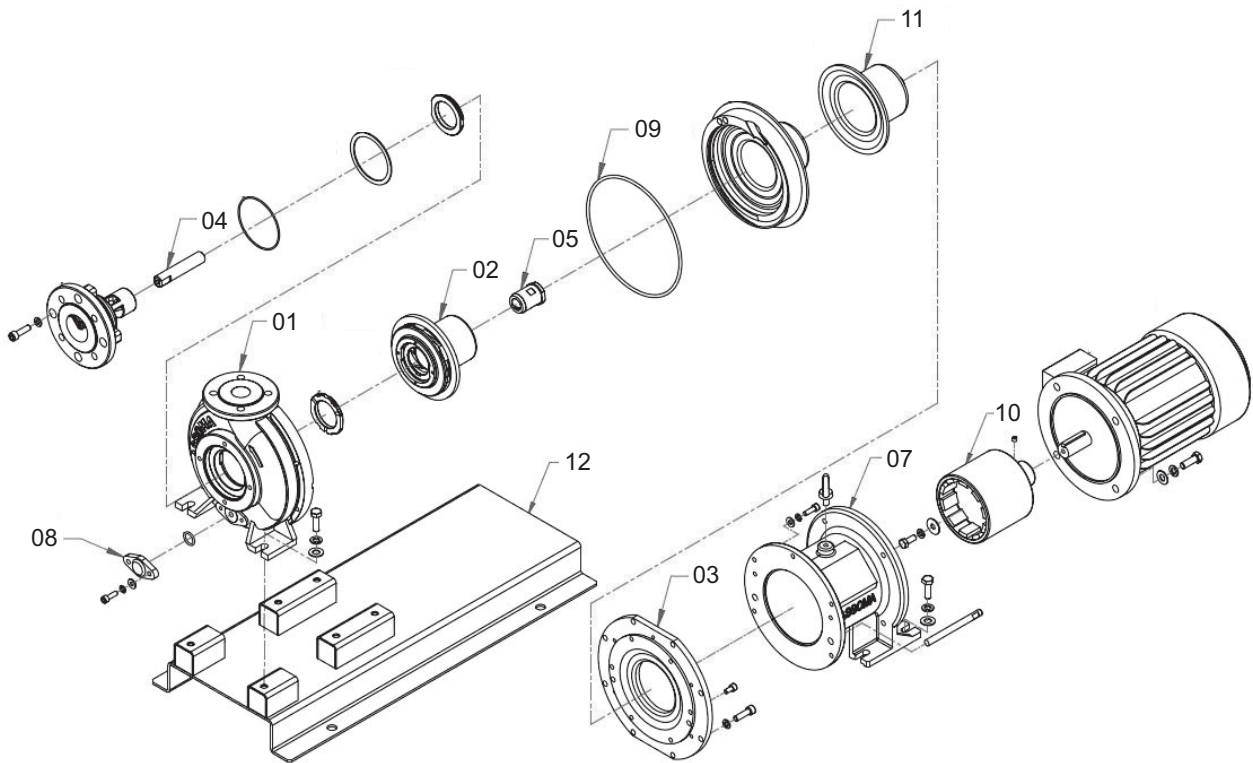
Teile (Explosionszeichnung), Baugröße 40..65
